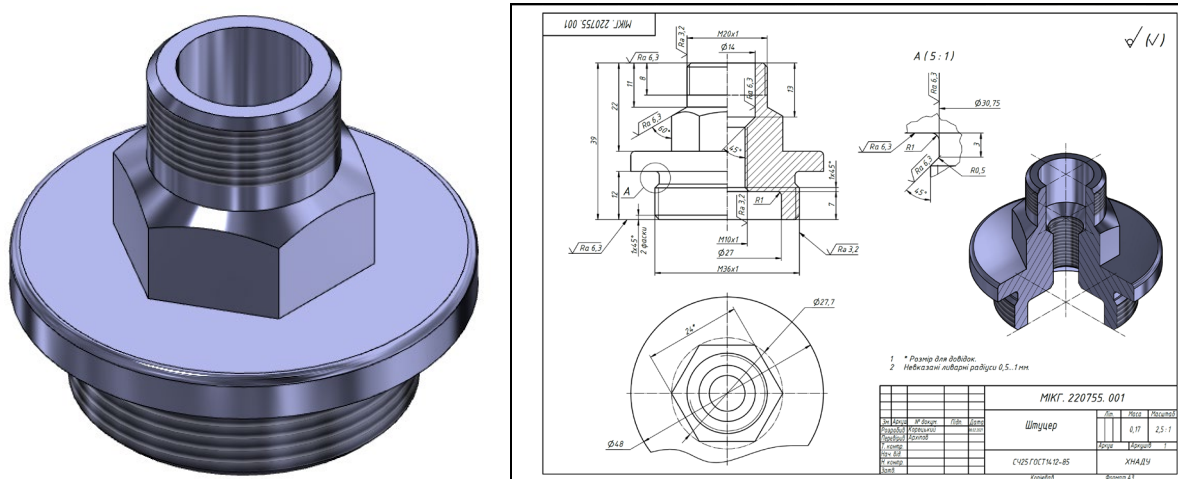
Модель та кресленник ливарної деталі з подальшою механічною обробкою.
